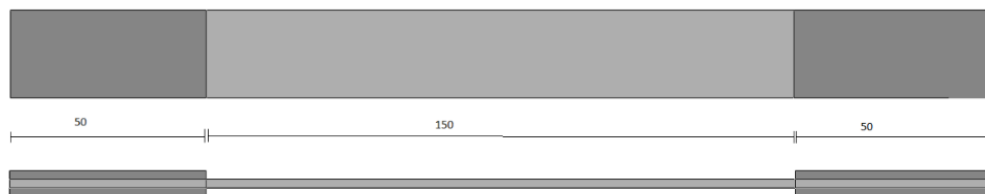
Dimensions (en mm) et géométrie des éprouvettes
